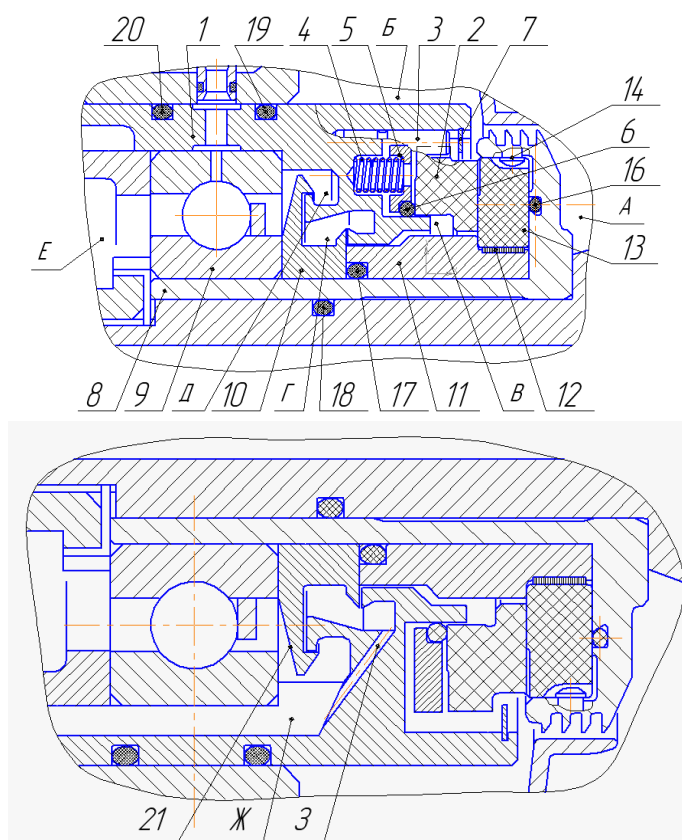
Конструктивная схема опорно-уплотнительного узла
